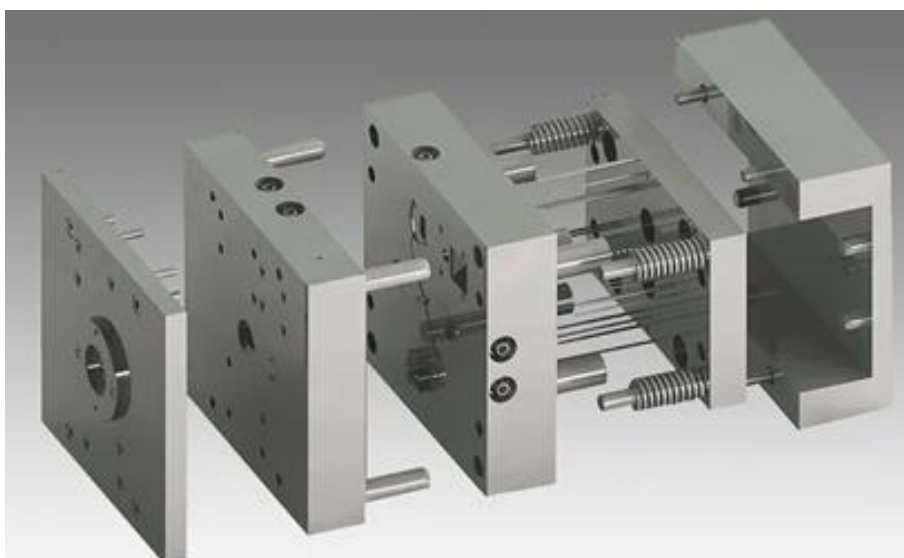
Конструкция пресс-формы для термопластавтомата
